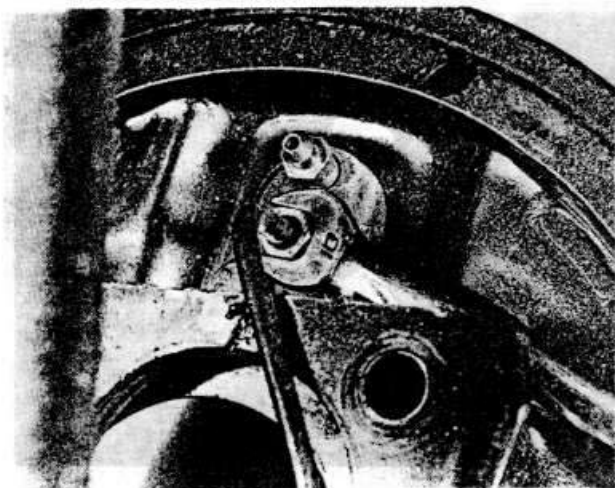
Отверните гайку трубопровода от заднего коленного цилиндра
